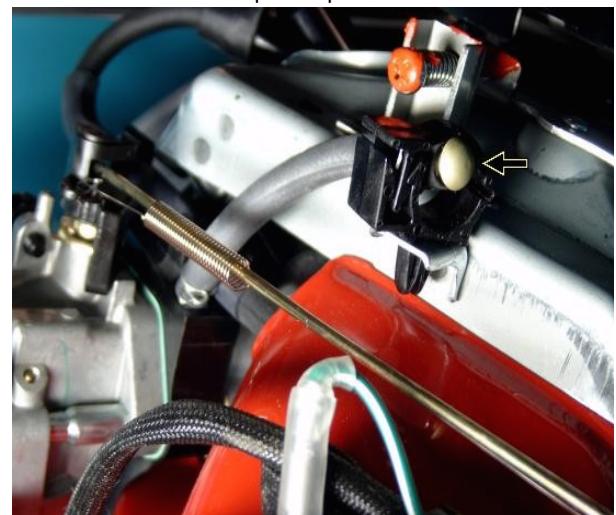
Установка заглушки вместо вакуумной пробки
